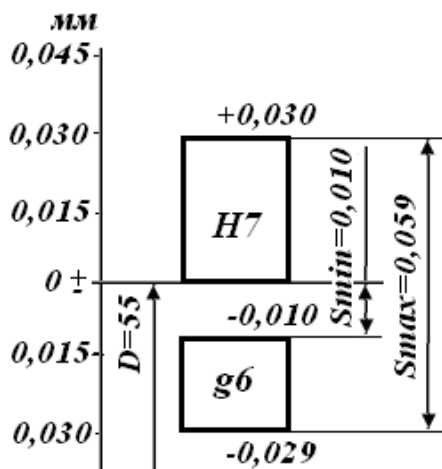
Схема розташування полів допусків з'єднання $\varnothing 55H7/g6$
